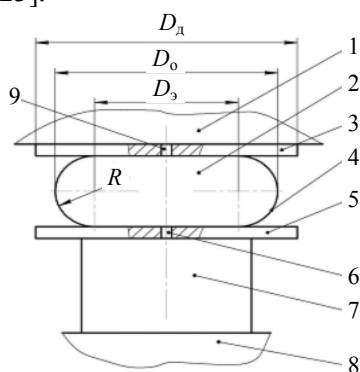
Пневморессора с повышенным демпфированием колебаний: 1 – кузов транспортного средства; 2 – пневморессора; 3, 5 – днище; 4 – гибкая оболочка; 6 – дроссельное отверстие; 7 – дополнительный резервуар; 8 – рама тележки; 9 – отверстие для питания пневморессоры сжатым воздухом
